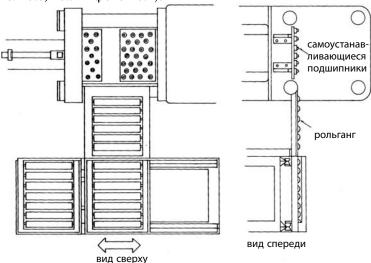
Стеллаж для установки кокилей и установка литья под давлением
